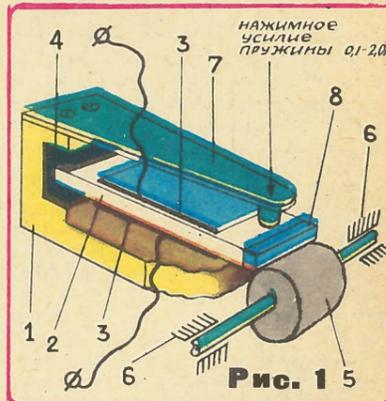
Конструкция пьезоэлектрического двигателя. Цифрами обозначены: 1 — корпус, 2 — пьезоэлемент, 3 — обкладки с проводами питания, 4 — виброгасящая прокладка, 5 — ротор, 6 — подшипники оси ротора, 7 — прижимная пружина, 8 — износостойкая насадка.
